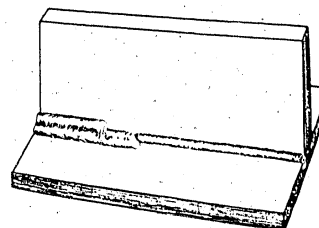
Kehlnaht-Mehrlagenschweißung
